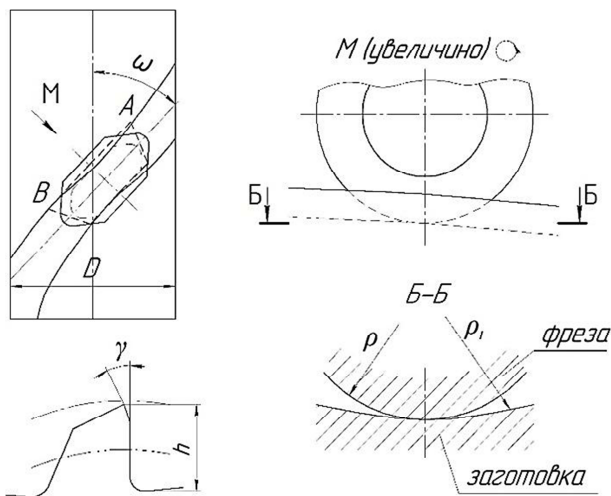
Схема фрезерования винтовых канавок двухугловыми фрезами
